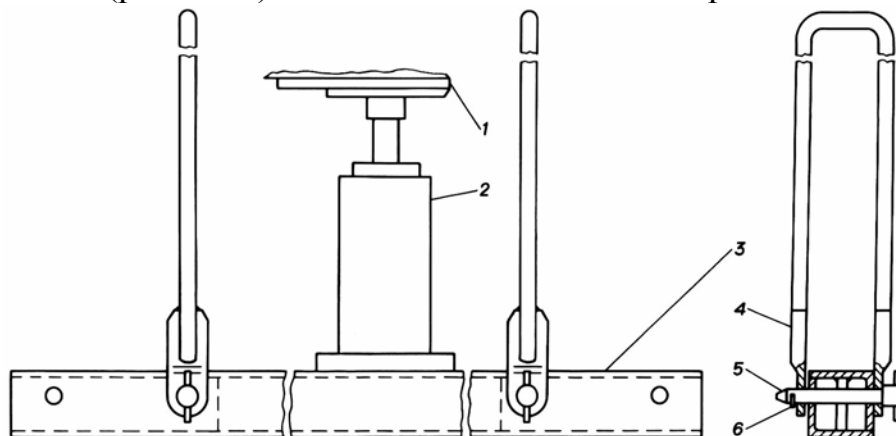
Приспособление для установки рессор: 1 – рессора; 2 – домкрат; 3 – балка; 4 – стремянки; 5 – палец; 6 – защелки
